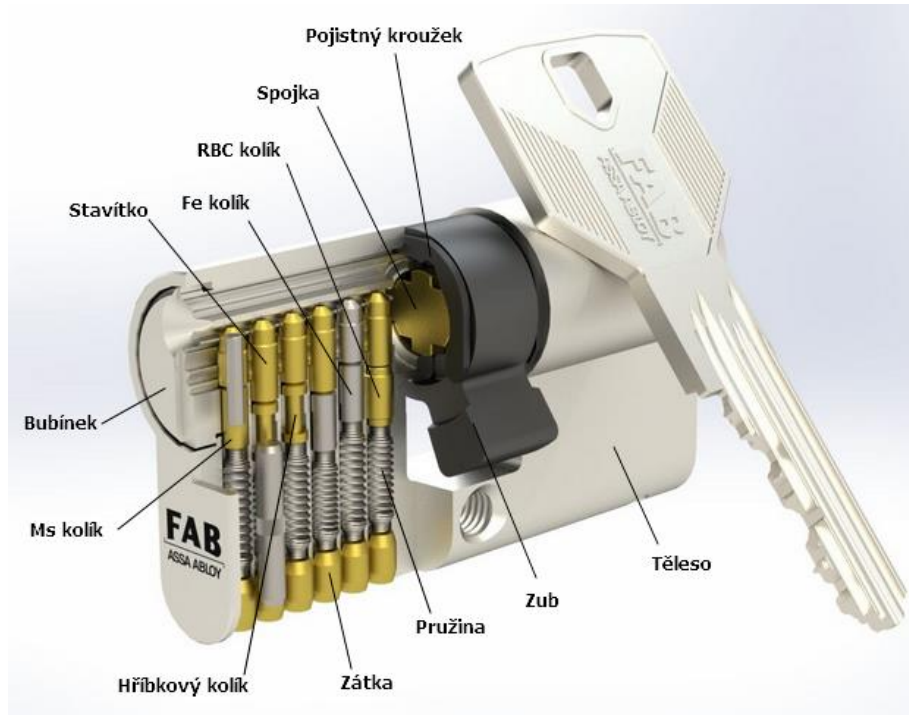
Princip odemknutí/zamknutí zámku [12].
